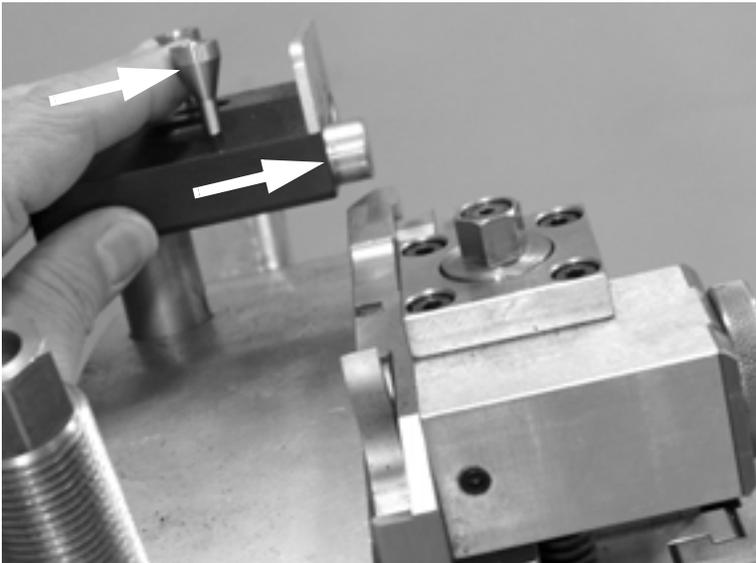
Drücken Sie den Auslöserknopf nach vor (in Richtung Werkzeugschlitten), um den Auslöserstift einzukuppeln.
